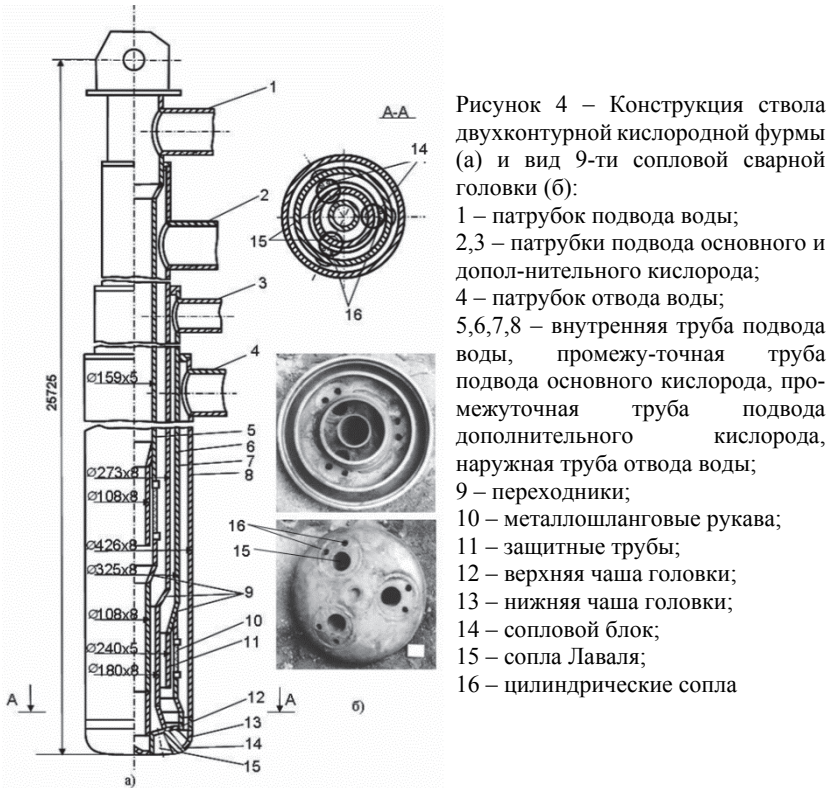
Конструкция ствола двухконтурной кислородной фурмы (а) и вид 9-ти сопловой сварной головки (б):
